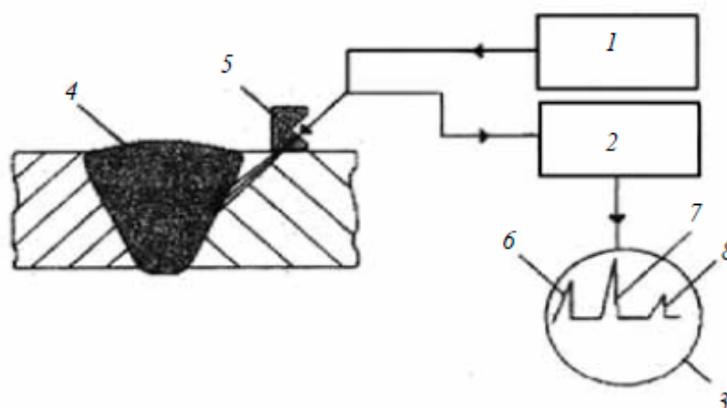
Ультразвуковой контроль сварных соединений: 1 – генератор; 2 – усилитель; 3 – экран прибора; 4 – сварной шов; 5 – искатель-приемник; 6 – начальный импульс;
